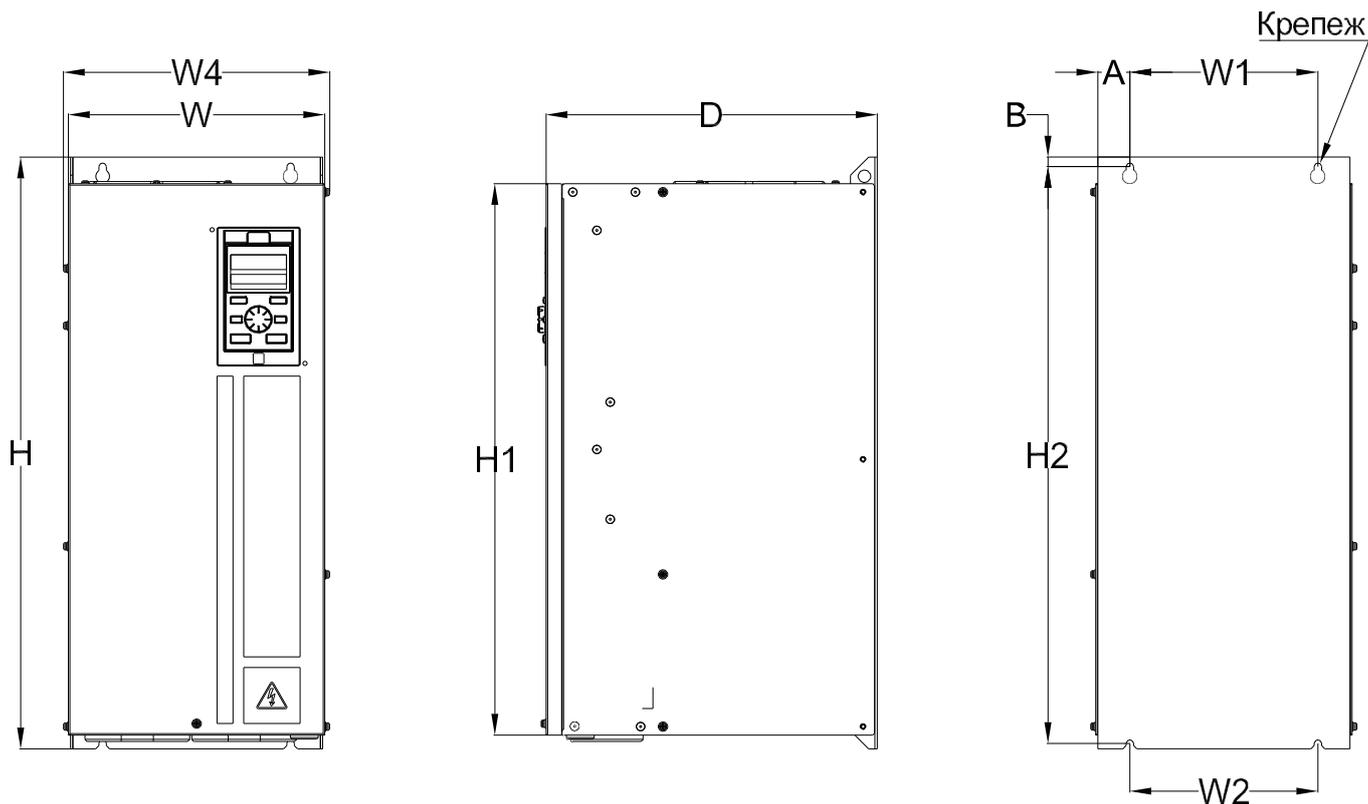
Чертеж преобразователя частоты, типоразмер B6
